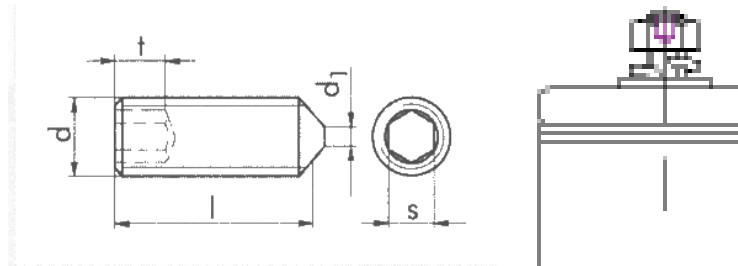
Gewindestab mit Innensechskant. Mit Hilfe von Loctide Kleber kann dieser in einer dauerhaften Änderung der Anschlussart von Innengewinde auf Stehbolzen abgeändert werden.
